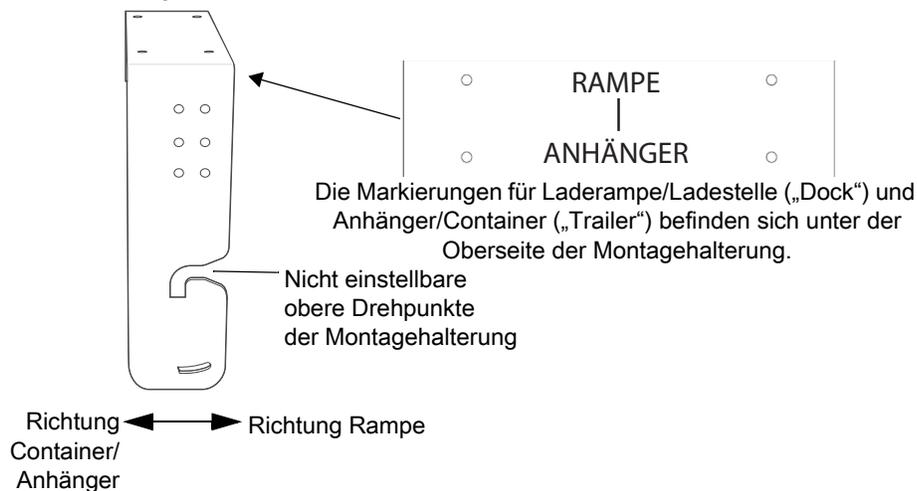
Befestigen der Zwischenhalterung für die Stange BR-000237-01
